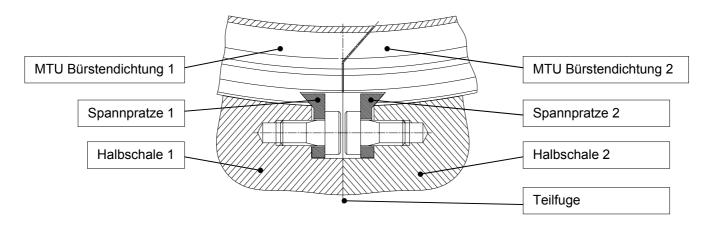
Segmentierte MTU Bürstendichtung (Beispiel Spannpratzen)
